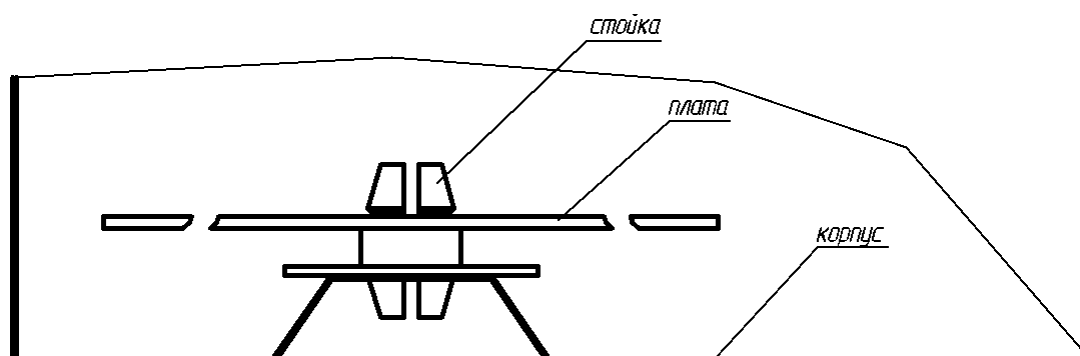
Установка платы в корпус на пластиковых стойках.
